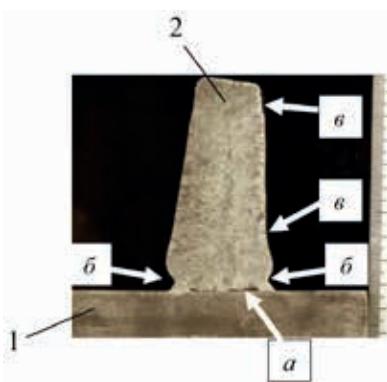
Поперечный макрошлиф опытного образца с дефектами: 1 – основной металл, 2 – наплавленный металл; стрелками показаны места непроваров основного металла (а), некачественного формирования галтелей (б) и рабочей поверхности наплавленного металла (в)
